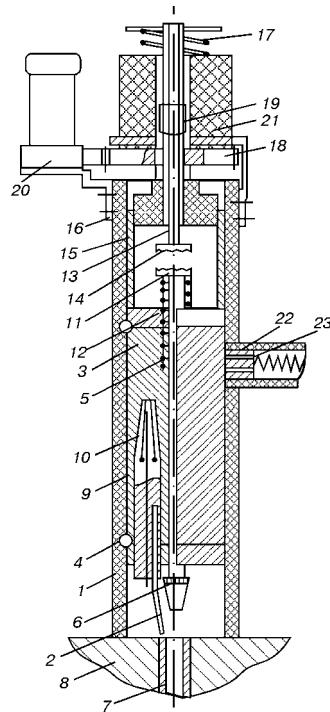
Автомат для сварки круговых швов малого диаметра (здесь и на рис. 2 обозначения см. в тексте)
